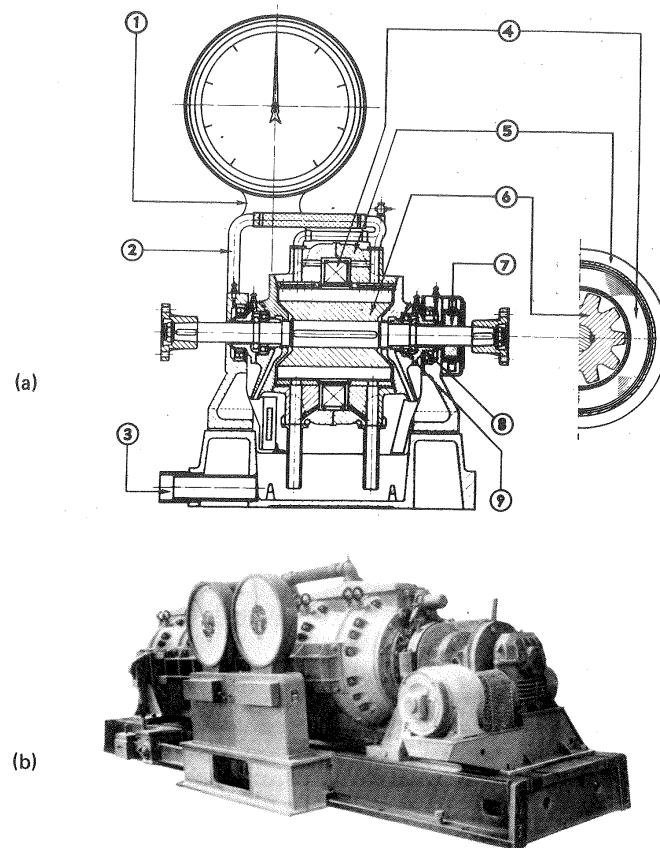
a) *Dinamómetro de inducción Heenan-Dynastic*: a) esquema: 1. Mecanismo de medición de par; 2. Entrada de agua; 3. Salida de agua; 4. Bobina; 5. Estator; 6. Rotor; 7. Generador del regulador; 8. Cojinete del muñón; 9. Cojinete del eje principal; b) Dos dinamómetros montados en tandem, con una capacidad de 4500 kW a 800/2500 rpm.
